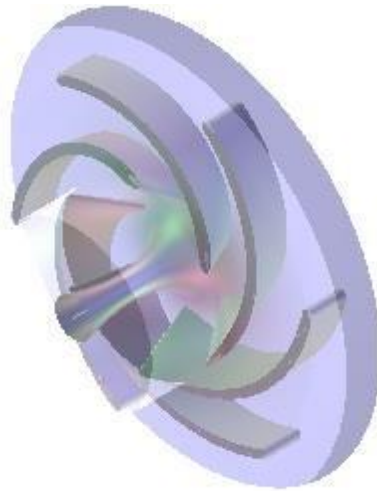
Géométrie en perspective de la roue (impeller).
